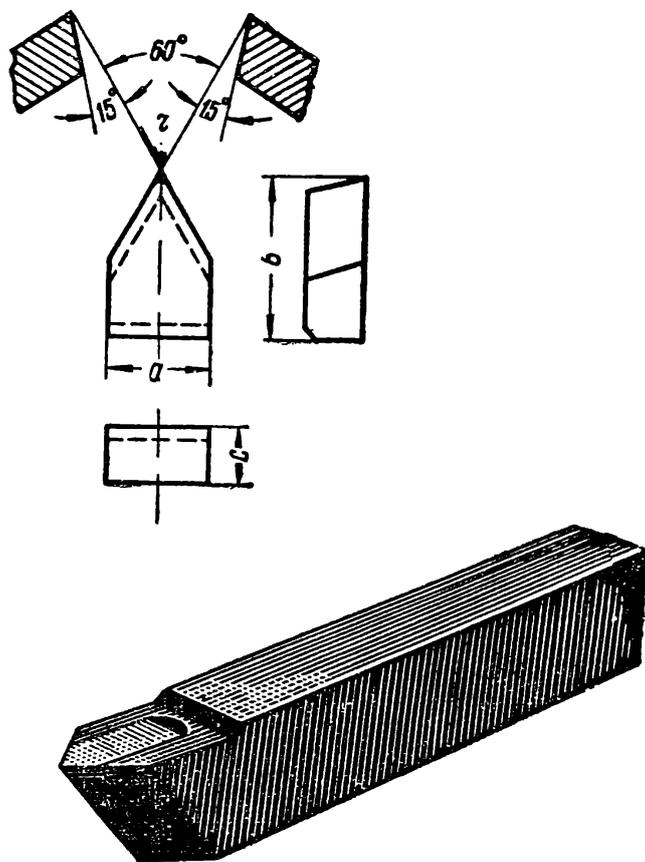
Форма 11 для резьбовых и чистовых резцов.
